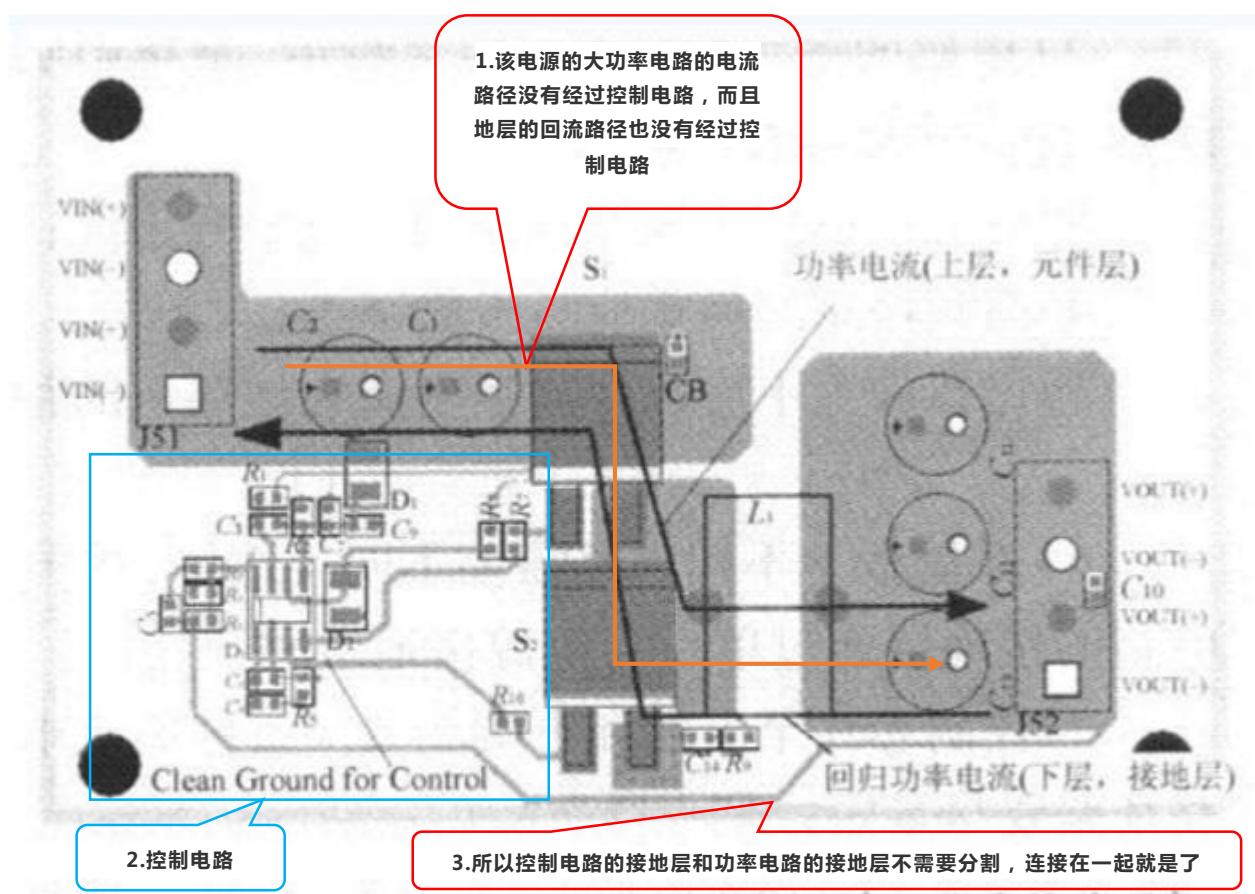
降压式开关电源 PCB 上层图(下层是接地层)
